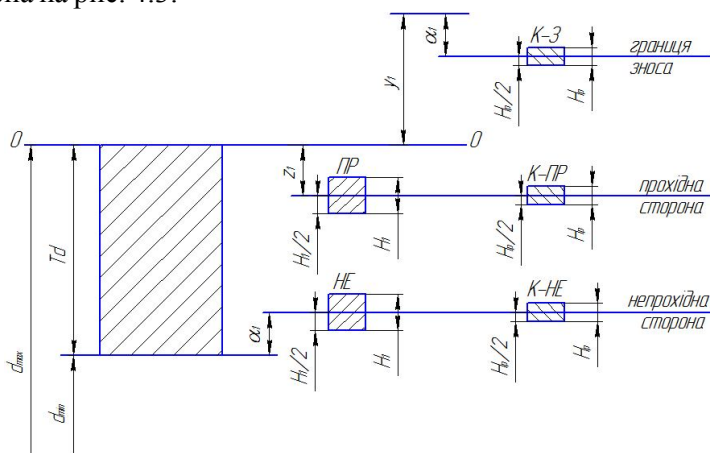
Схема розташування полів допусків калібрів для контролю вала
